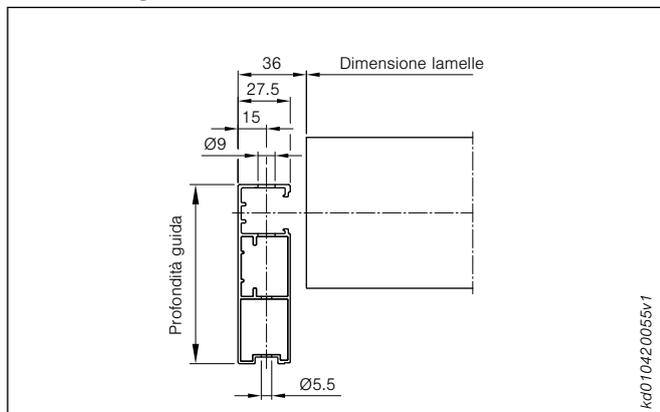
Fori di fissaggio/dimensione lamelle profilato guida
